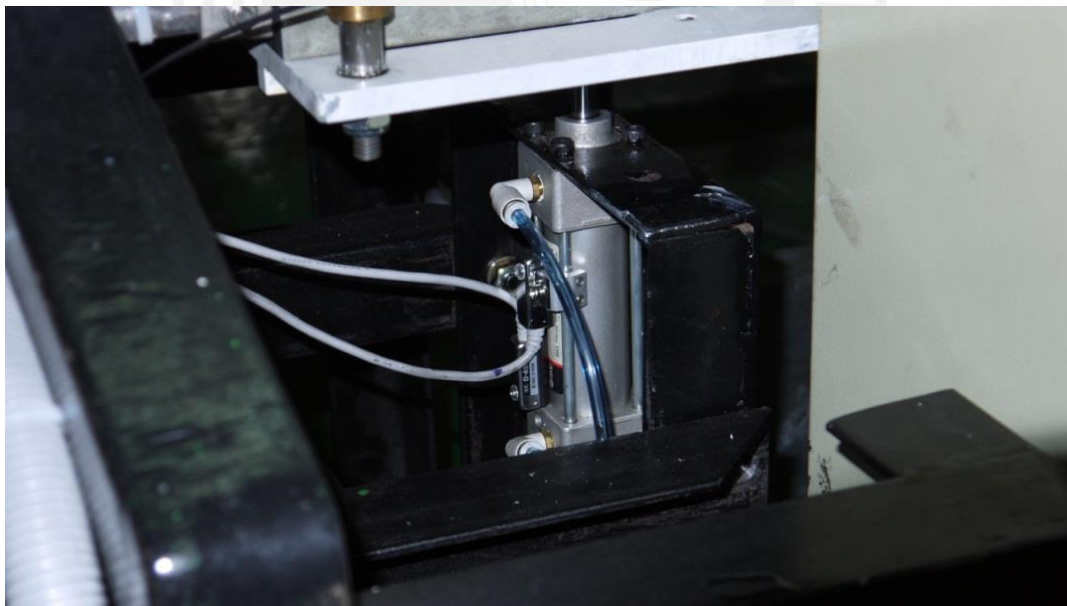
Detalle del cilindro neumático de elevación de plataforma en máquina llenadora
